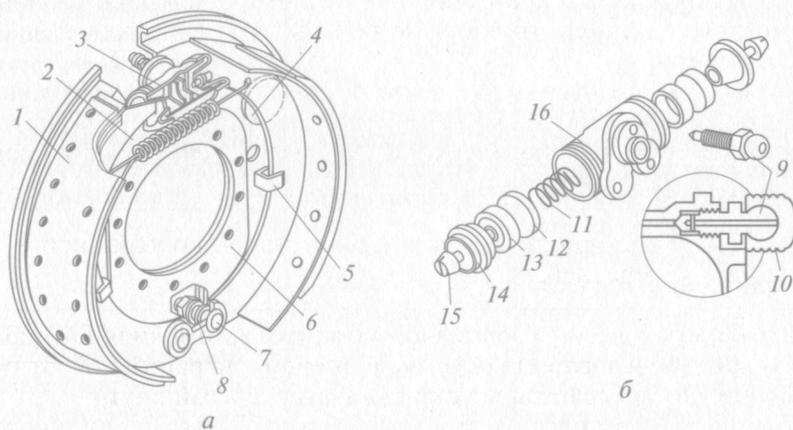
Колесный тормозной механизм (а) и колесный тормозной цилиндр (б) автомобиля ГАЗ-53А:
